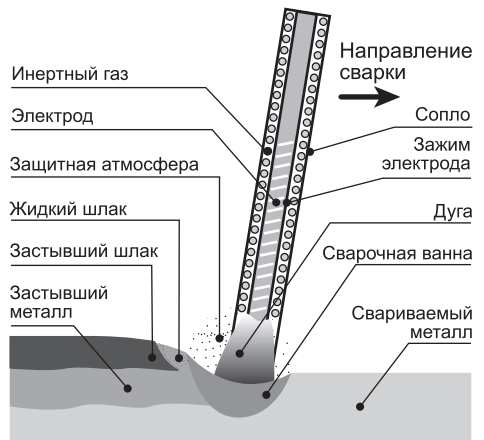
Схема процесса ручной дуговой сварки в инертном газе неплавящимся электродом
